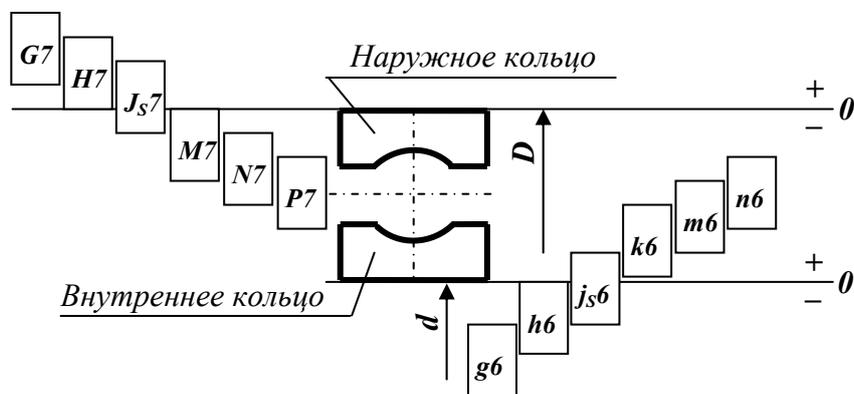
Поля допусков отверстия и вала при монтаже подшипника.
